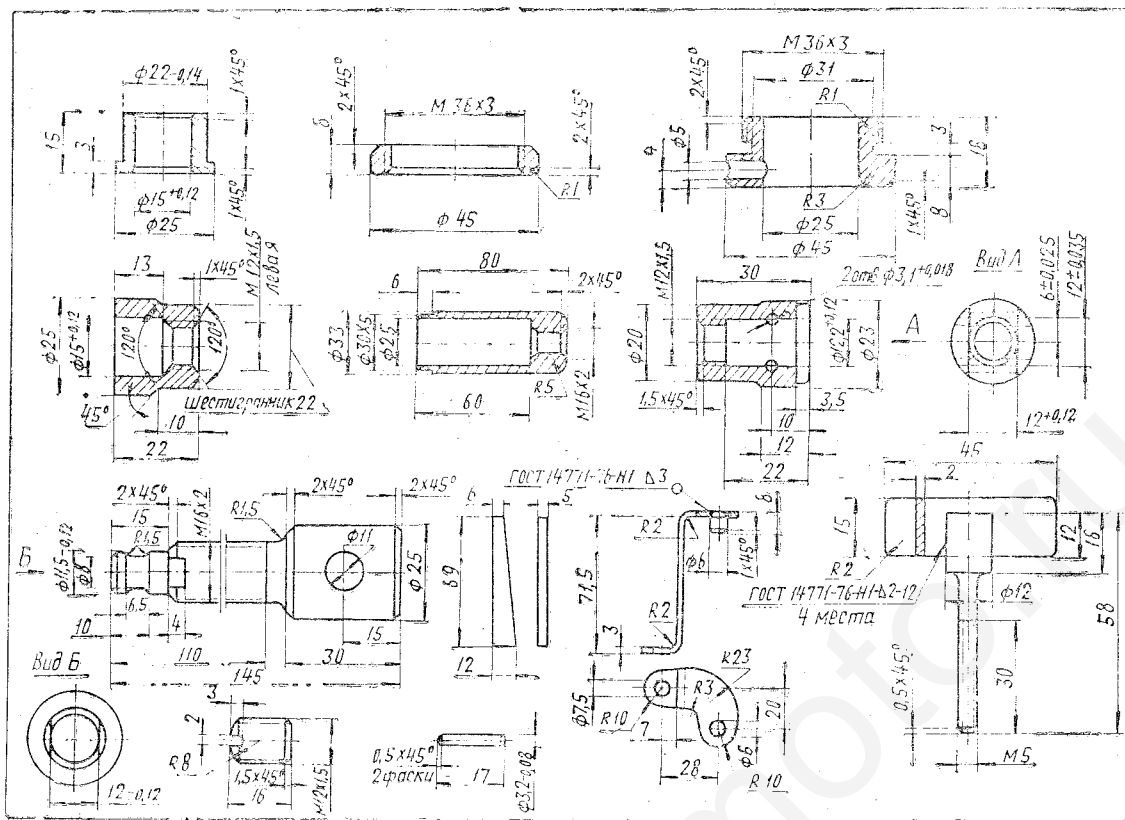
Приспособление для распрессовки и запрессовки коленчатого вала разъединения половин картера
